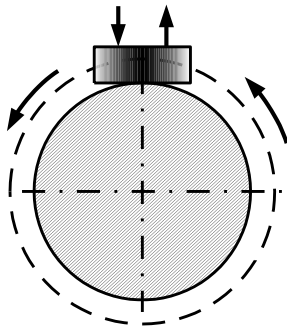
Ультразвуковий імпульсний вимірювальний пристрій
